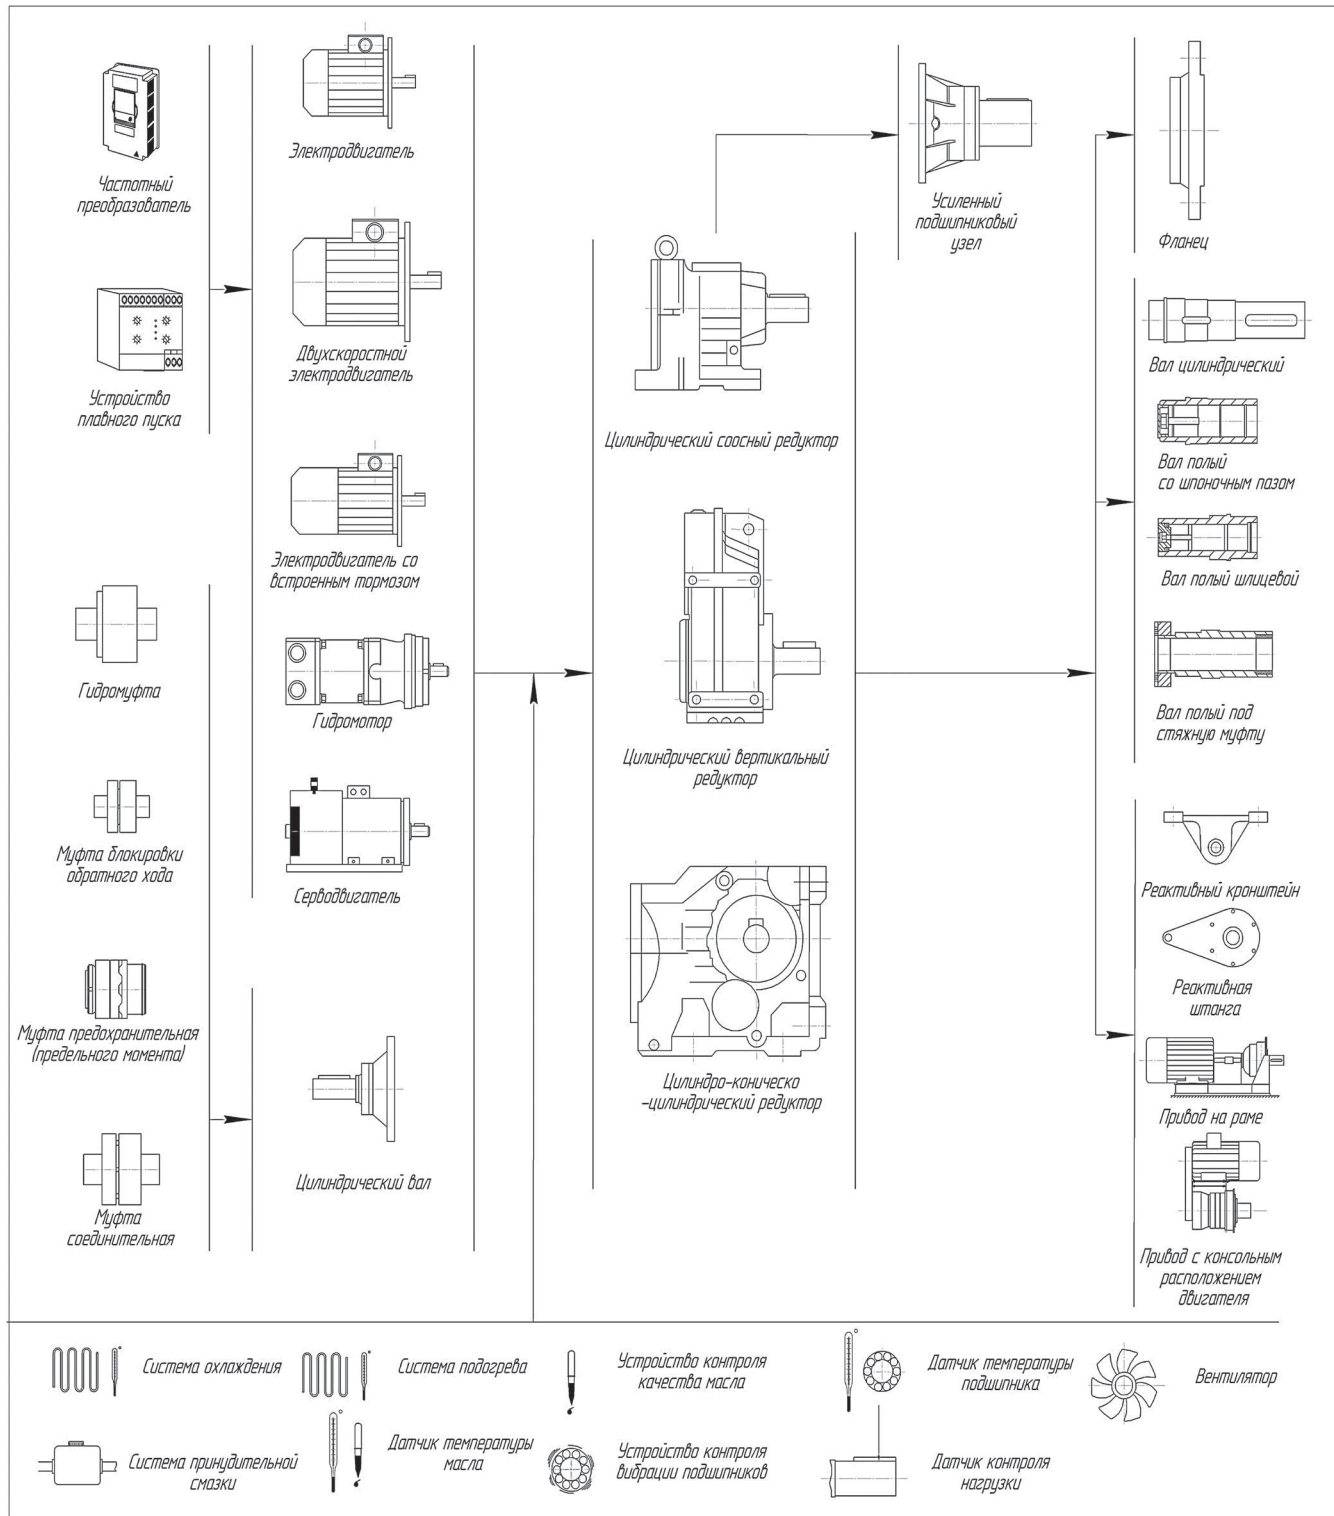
Блочно-модульная схема построения цилиндрических редукторов и мотор-редукторов.
